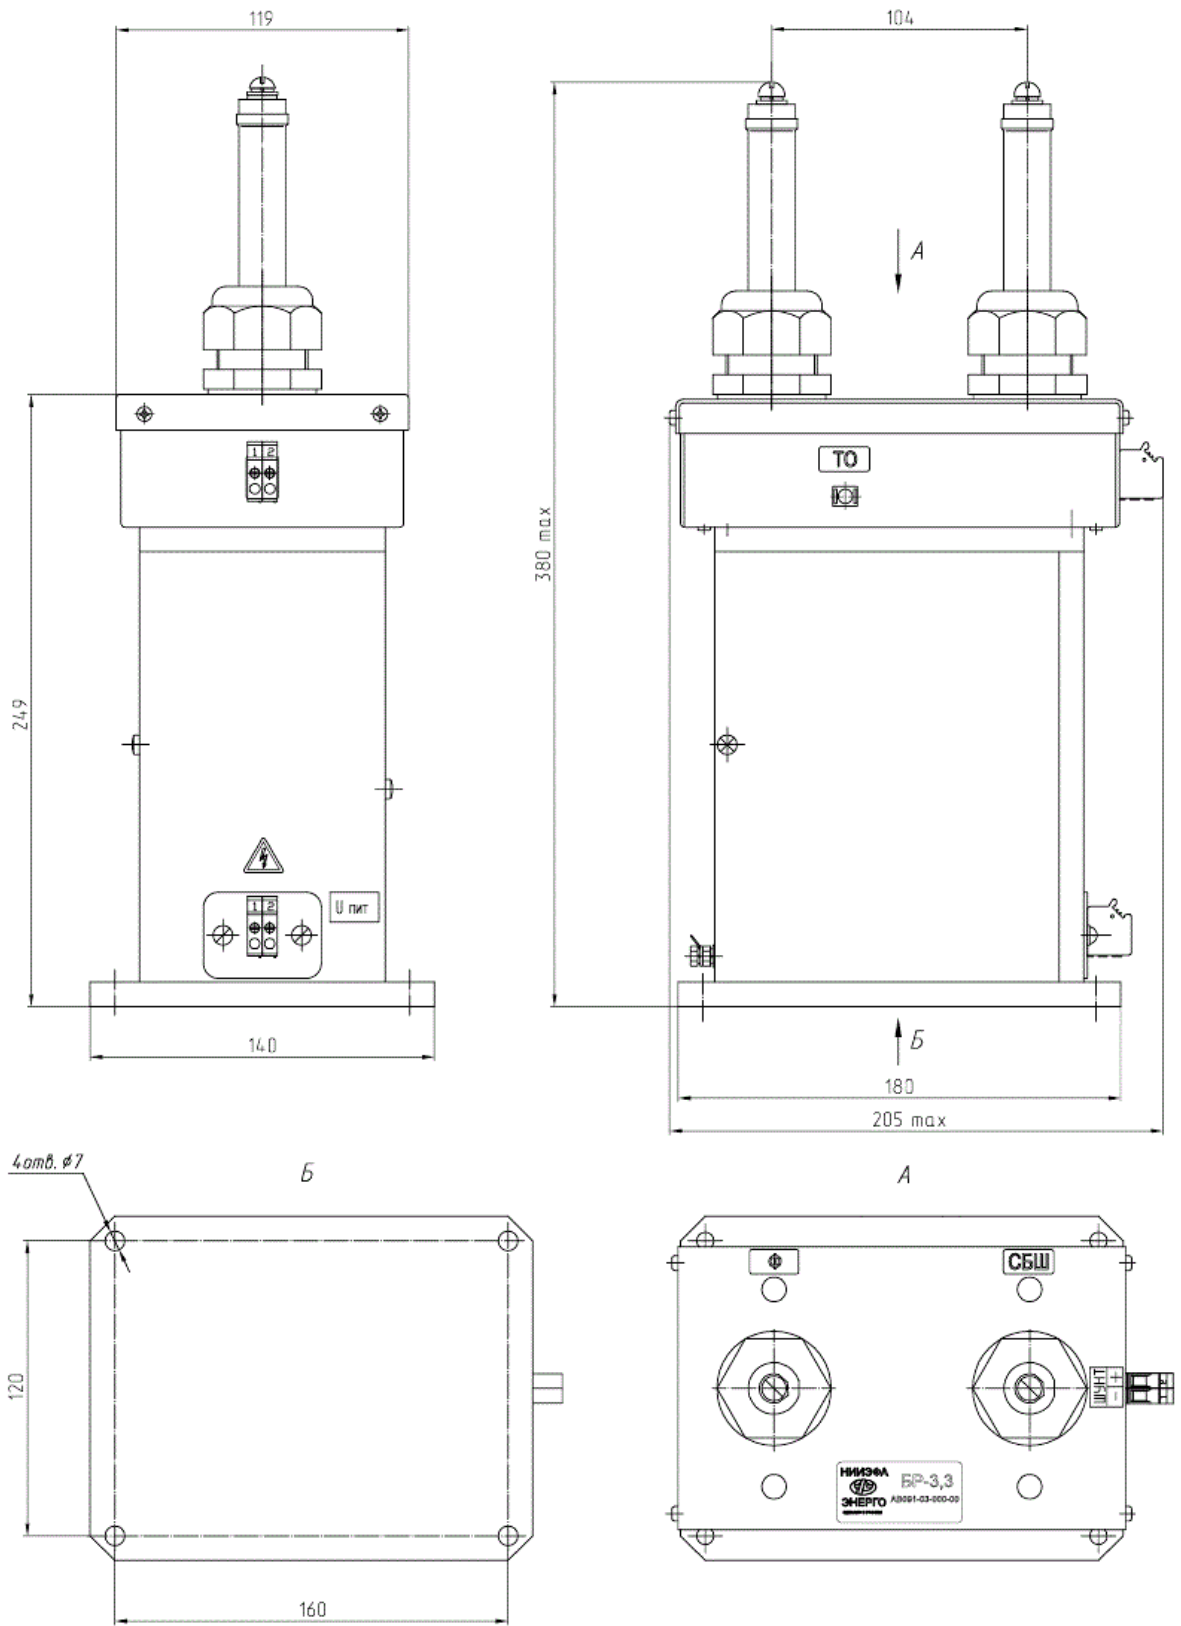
Габаритные и установочные размеры блока БР-3,3
